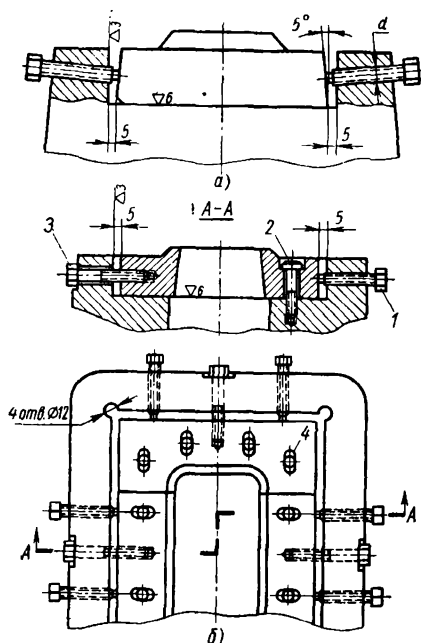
Крепление матрицы винтами: а — цельной или из двух секций; б — из трех секций и более; 1 — стопорный винт; 2 — винт крепления матриц; 3 — натяжной болт; 4 — отверстие под винт крепления матрицы
